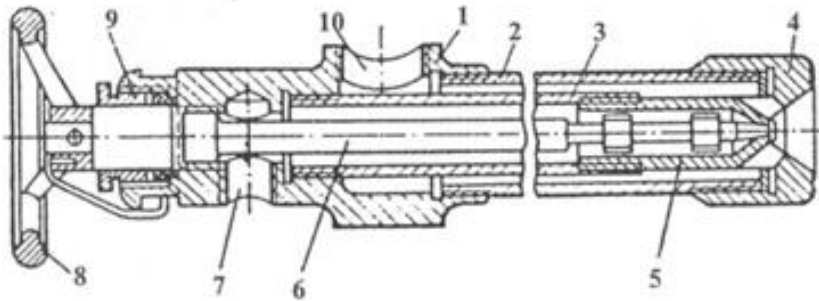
Форсунка для спалювання рідкого палива: 1 – корпус; 2 – зовнішня труба розпилювача; 3 – внутрішня труба для палива; 4 – зовнішнє сопло; 5 – внутрішнє сопло; 6 – голка; 7 – отвір для подачі палива; 8 – штурвал; 9 – натискна гайка; 10 – отвір для подачі повітря.
